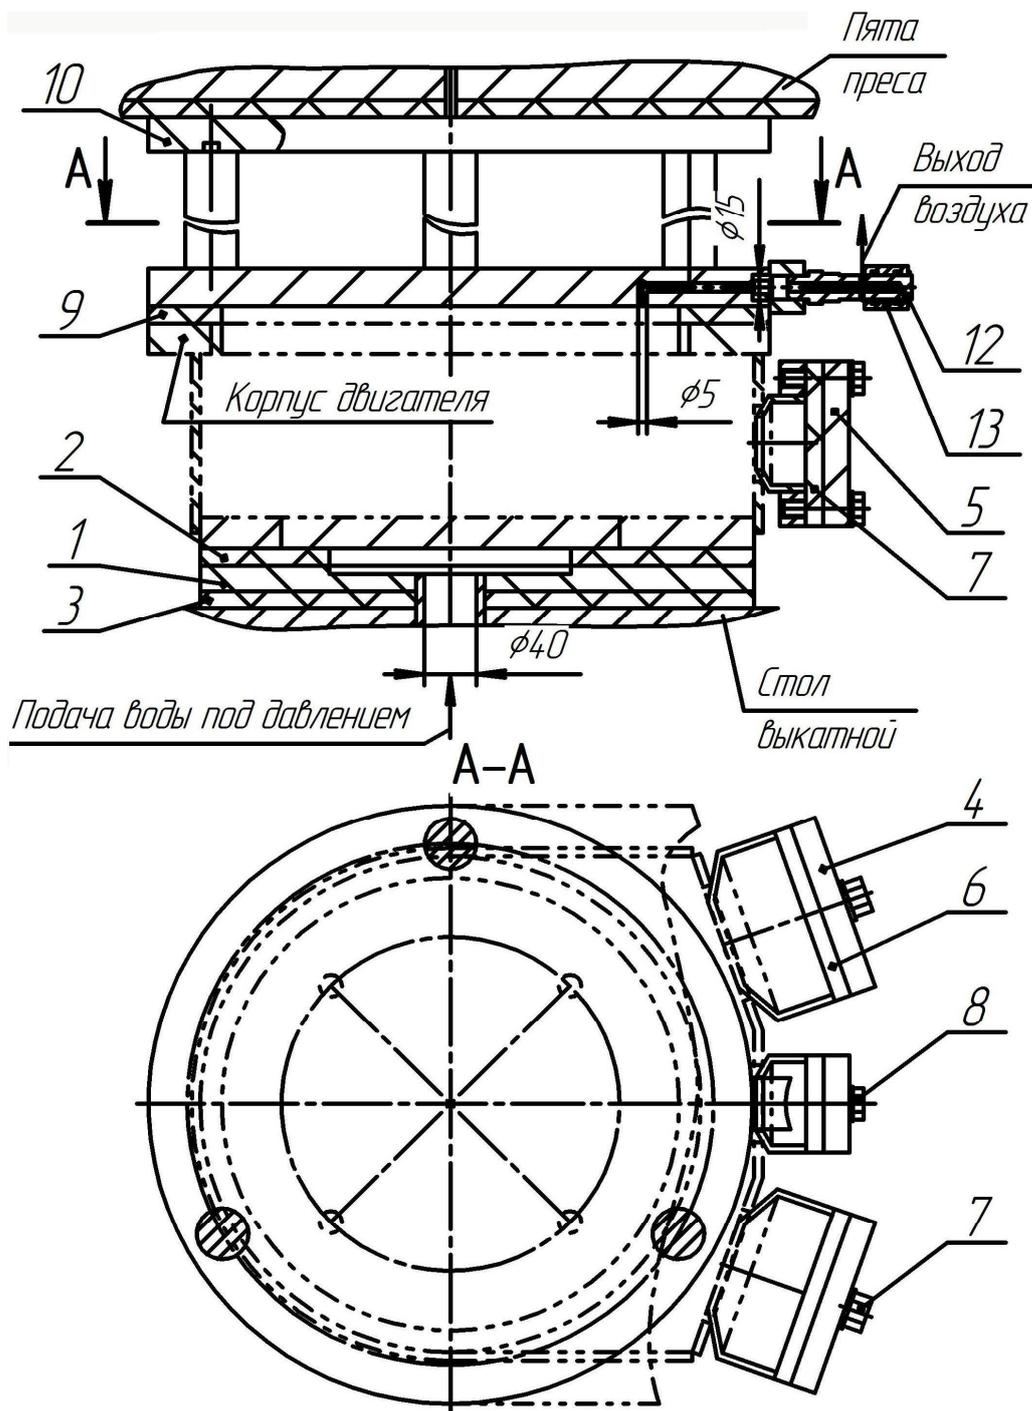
Приспособление для гидроиспытания корпуса двигателя 2АКДВ250М4; В4
